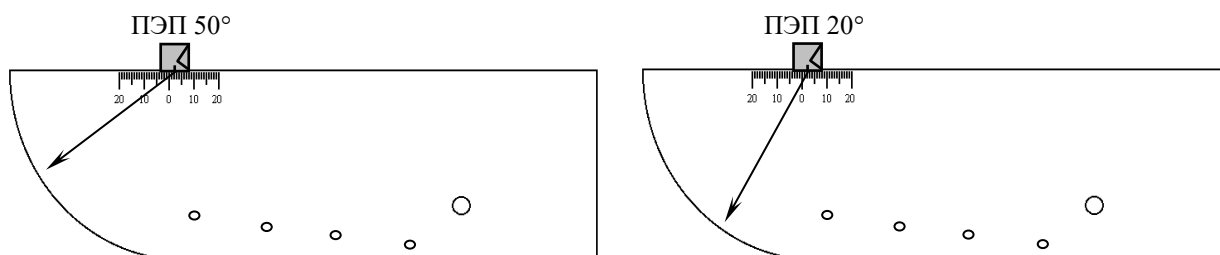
Схема установки наклонного ПЭП на стандартный образец СО-3Р при настройке глубиномера для ПЭП 20° и 50°
